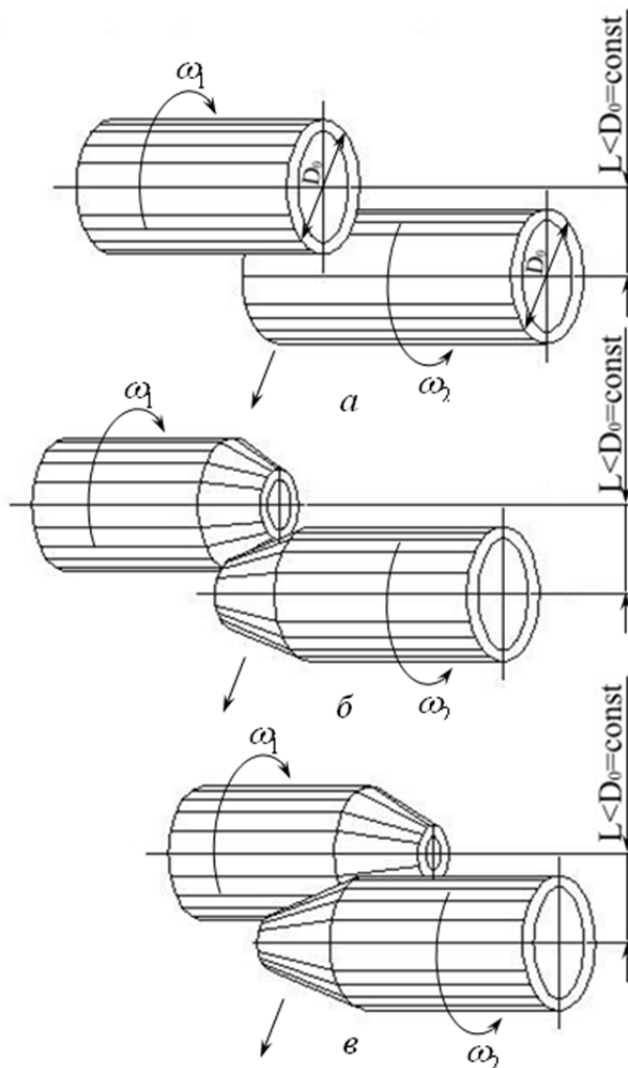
Получение конусов при взаимной обкатке трубчатых заготовок:
